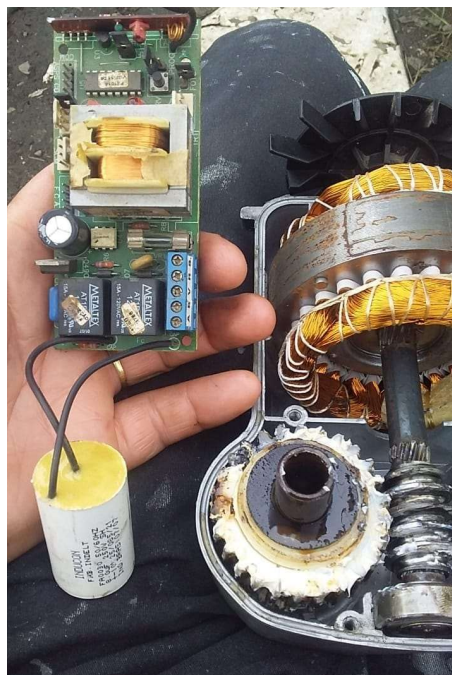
Primeiro Motor testado - Motor Basculante ¼ HP
